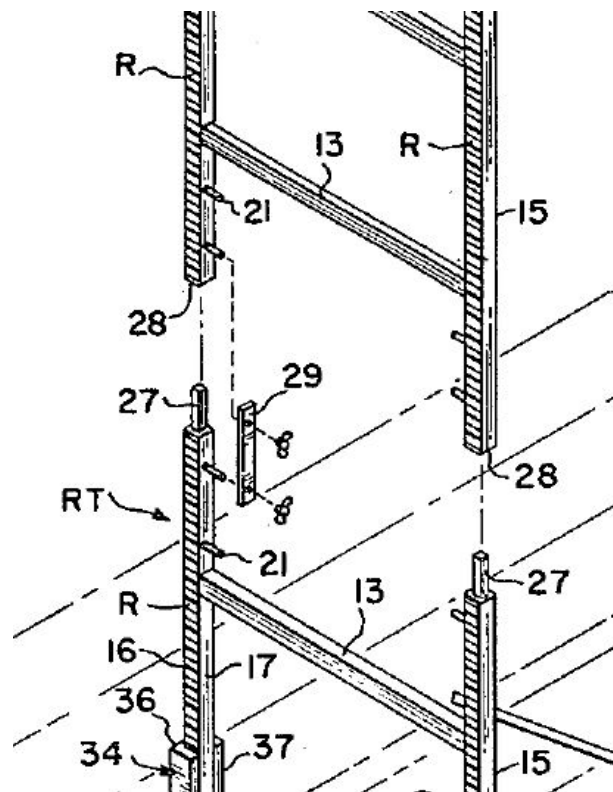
Lösung für die Befestigung der Zahnstangenteile [52]
